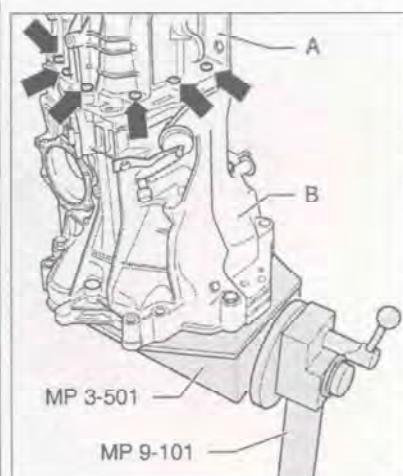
Отверните болты (стрелки) и отделяйте корпус коробки передач (A) от картера сцепления/главной передачи (B).
